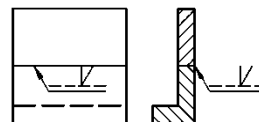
Ejemplo 2, Soldadura a tope
